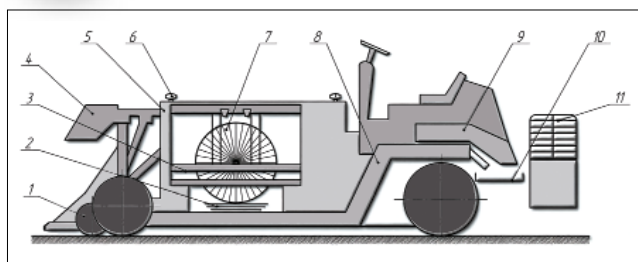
Схема устройства комбайна МПЯ: 1 – формователь; 2 – поперечный транспортер; 3 – вибратор; 4 – шасси; 5 – рама; 6 – подъемное устройство; 7 – активатор; 8 – продольный транспортер; 9 – система очистки; 10 – разгрузочная площадка; 11 – кассета с ящиками
